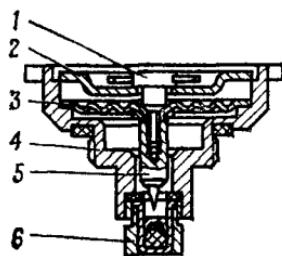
Взрыватель ВПМ-П для пассивной подледной мины:
